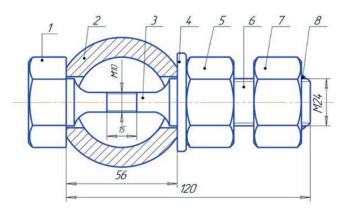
Конструкция болтов с ослаблением и двумя гайками для испытаний болтов с диаметром резьбы M24: 1 — головка болта; 2 — динамометр; 3 — ослабленная часть болта с резьбой M10; 4 — шайба; 5 — гайка; 6 — резьбовая часть болта; 7 — реактивная гайка; 8 — сварка
